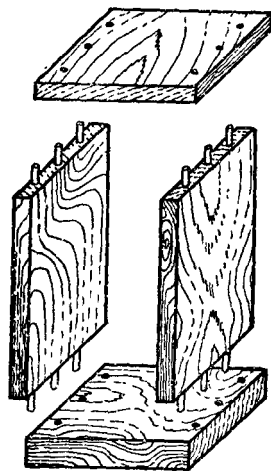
Соединение стенок шкафчика на круглых нагелях.
